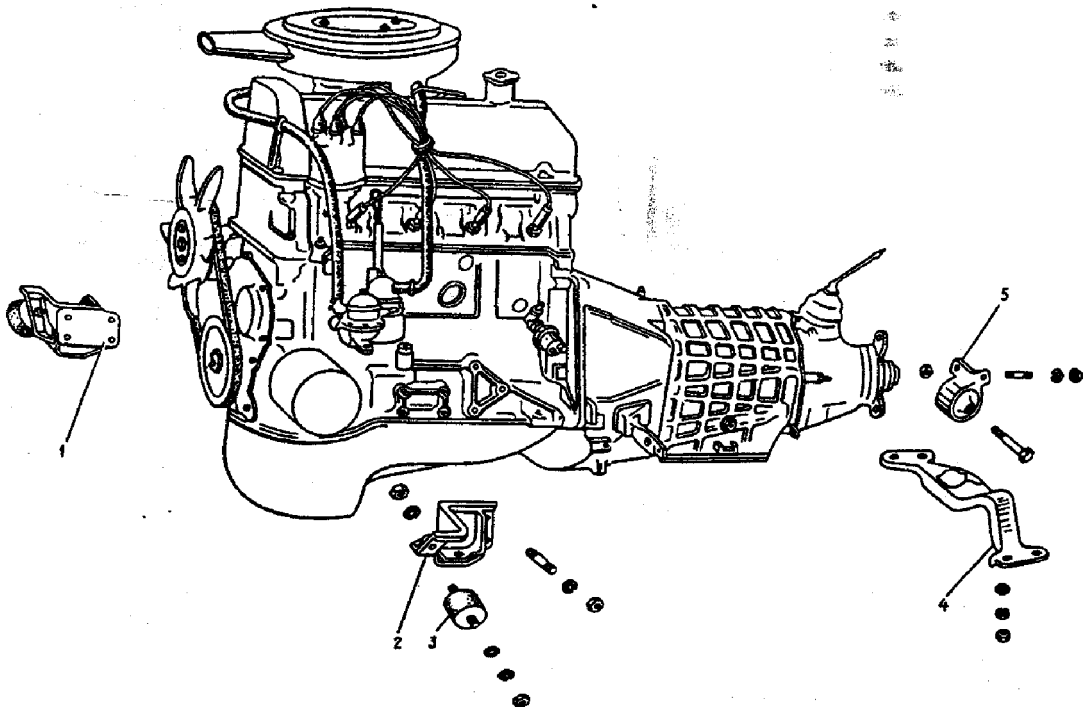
Fixação do motor: 1 - suporte direito do motor com coxim; 2 - suporte esquerdo do motor; 3 - coxim; 4 - travessa de fixação traseira do motor; 5 - suporte traseiro do motor com apoio.
